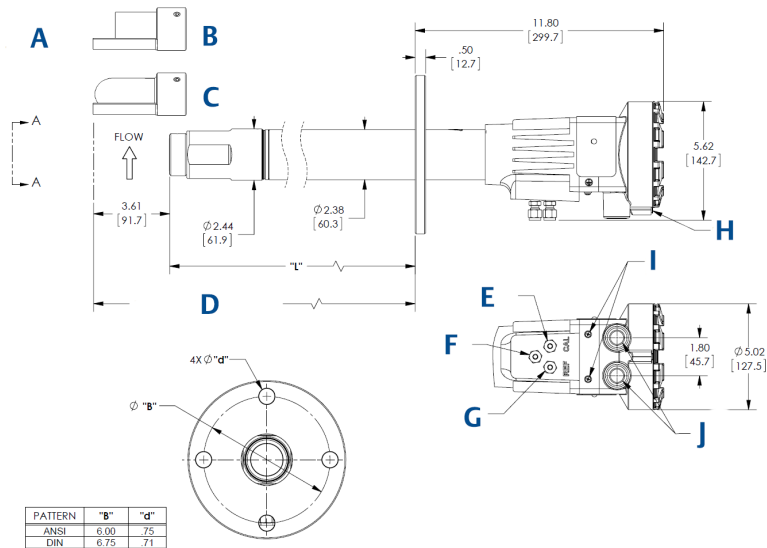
Rosemount 6888A с корпусом автоматической калибровки для полевых подключений — выход HART
